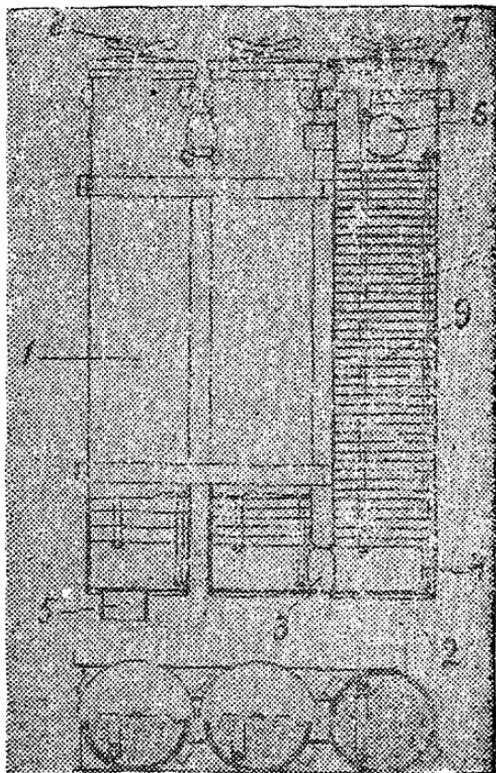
Пластинчатый очиститель в сборе: 1—корпус цилиндра; 2—дно цилиндра; 3—соединительный патрубок; 4—соединительные фланцы; 5—патрубок ввода газа; 6—патрубок вывода газа; 7—крышка; 8—барашек; 9—секции пластинчатых очистителей.
